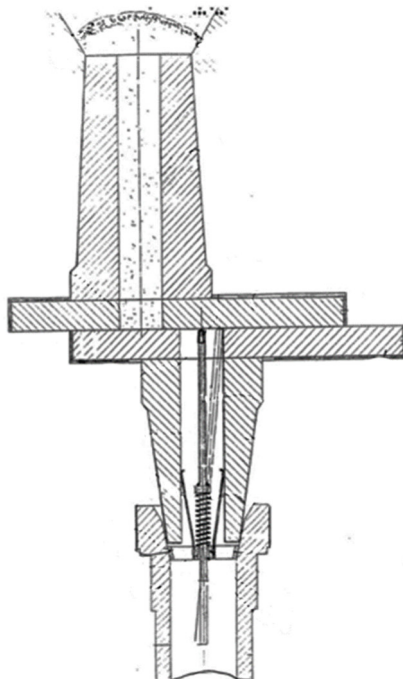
Катапульта, предназначенная для разрушения твердой корки на стартовой смеси при разливке с погружным стаканом
